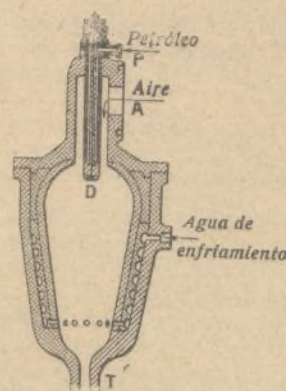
Cámara de combustión de la turbina Armengaud-Lemále
